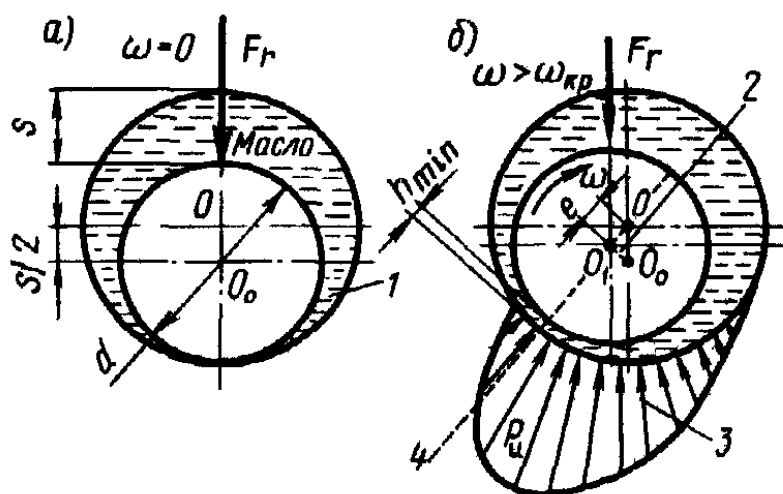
Гидродинамическая смазка подшипника скольжения
